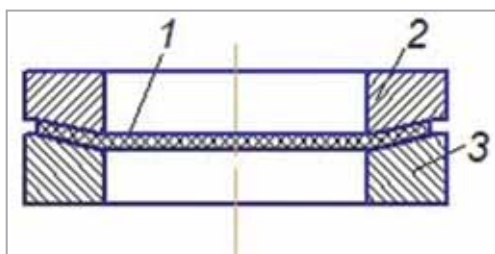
Схема размещения предохранительной мембраны газового баллона:
